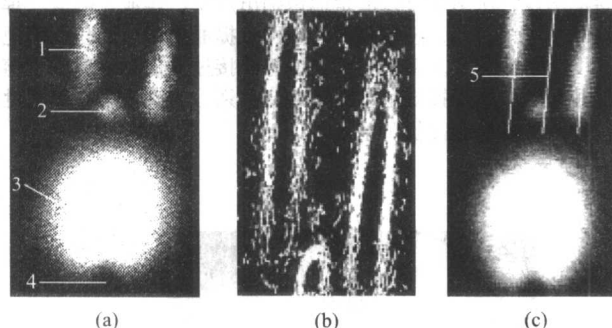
TIG 焊焊缝图像及其处理
